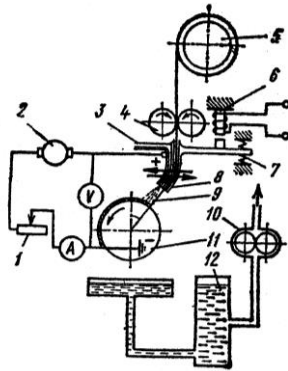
Схема установки для автоматичної вібродугової наплавки:
